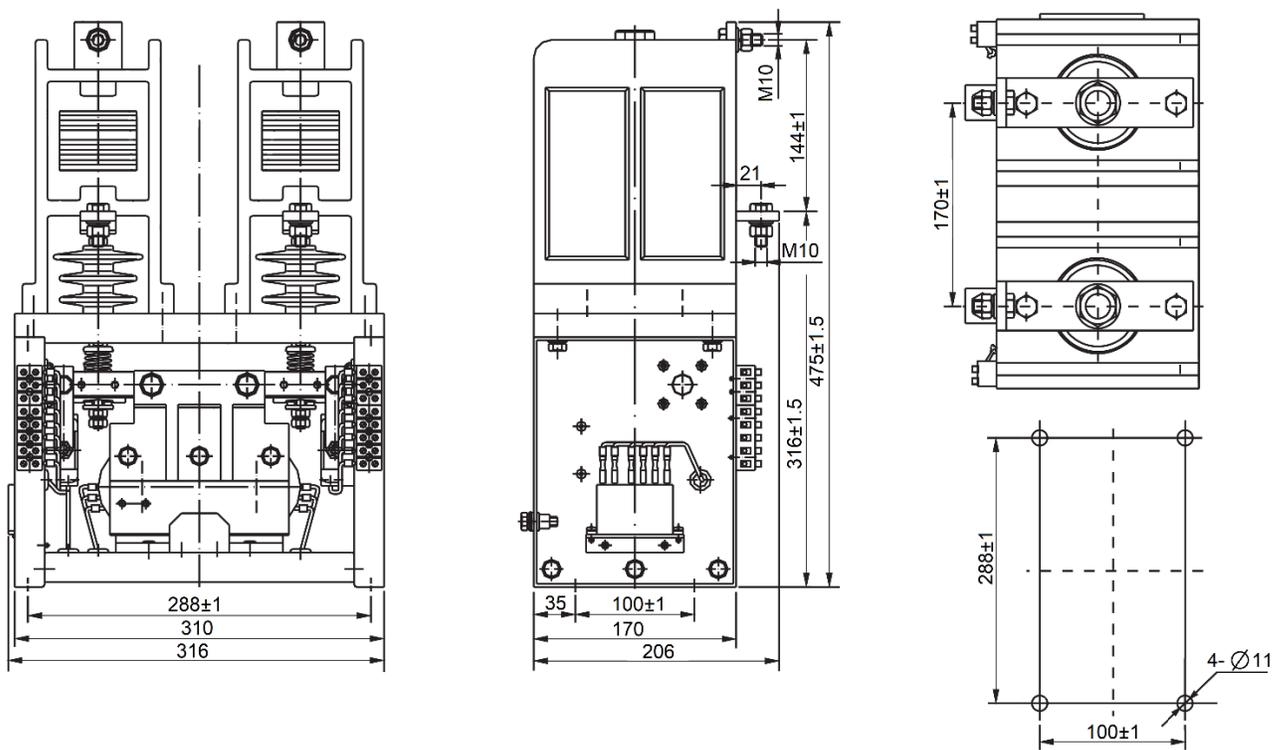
Габаритные размеры контакторов КВТ-6 на номинальные токи 160, 250, 400, 630 А двух полюсного исполнения и размеры монтажной площадки.
